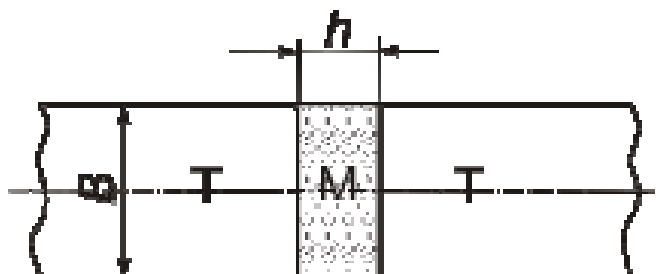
Схема сварного соединения с мягкой прослойкой
